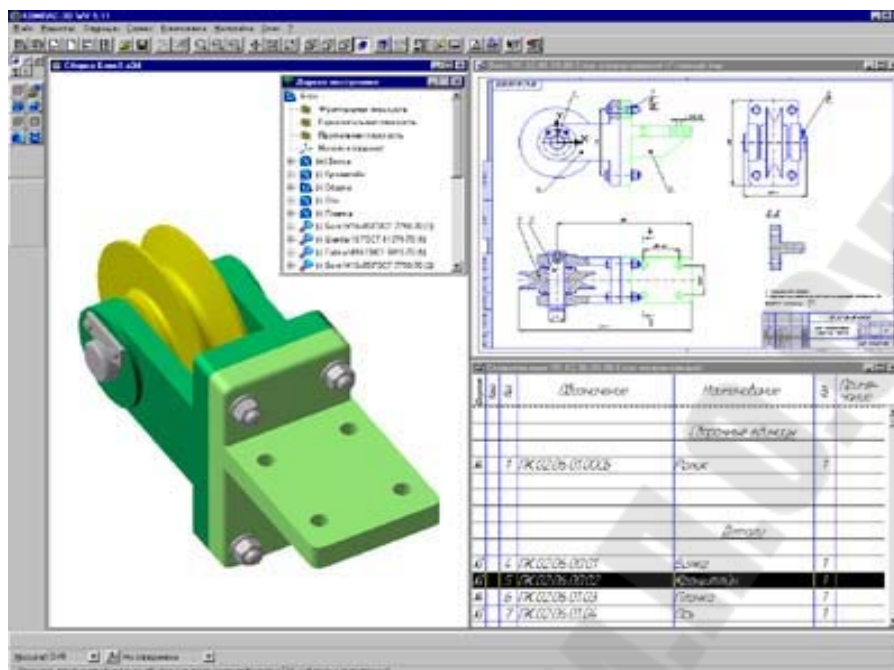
Ассоциированный чертеж упора роликового.
